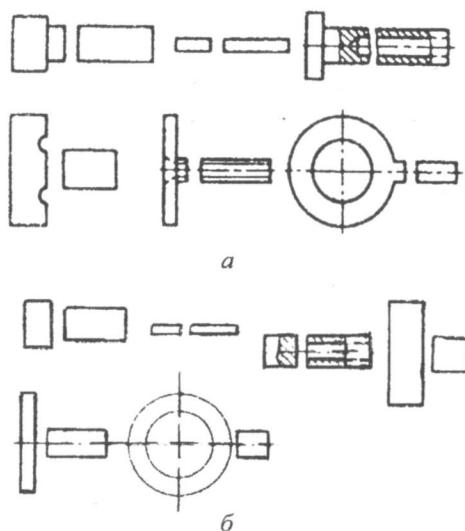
Типы сварных соединений, выполняемыхстыковой сваркой: *a* – сопротивлением;
